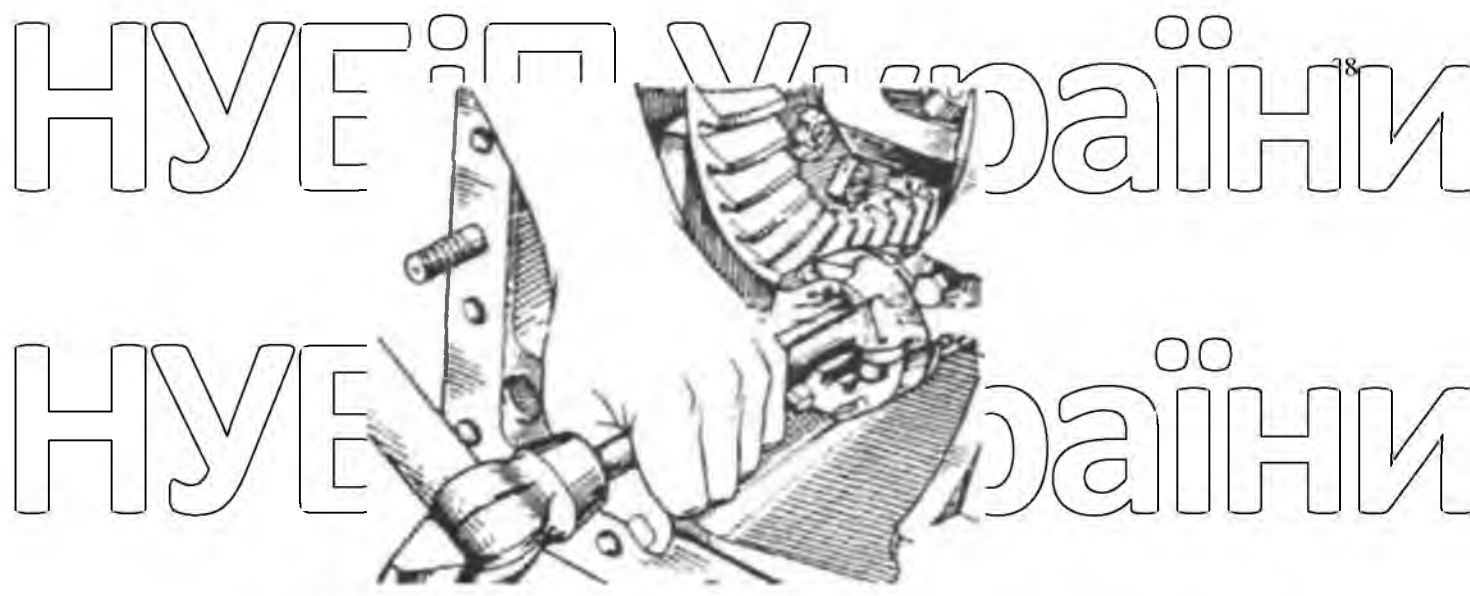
Вибивання вала коронної шестерні в зборі з шестернею, склячкою і підшипником.
